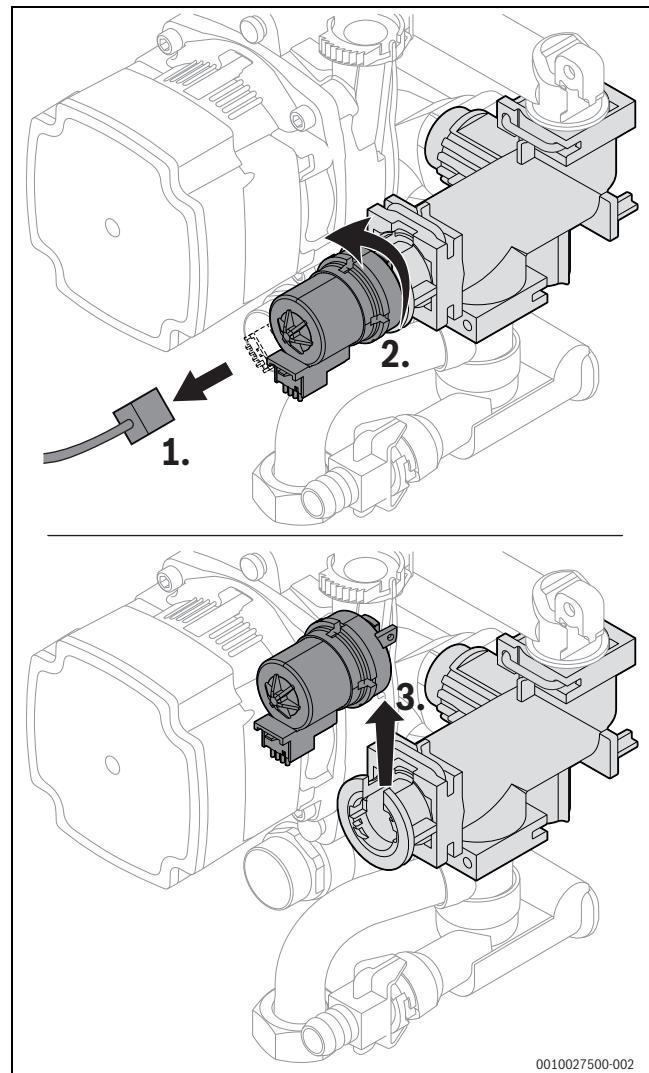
Démonter le moteur au niveau de la vanne sélective (variante sans vis)
